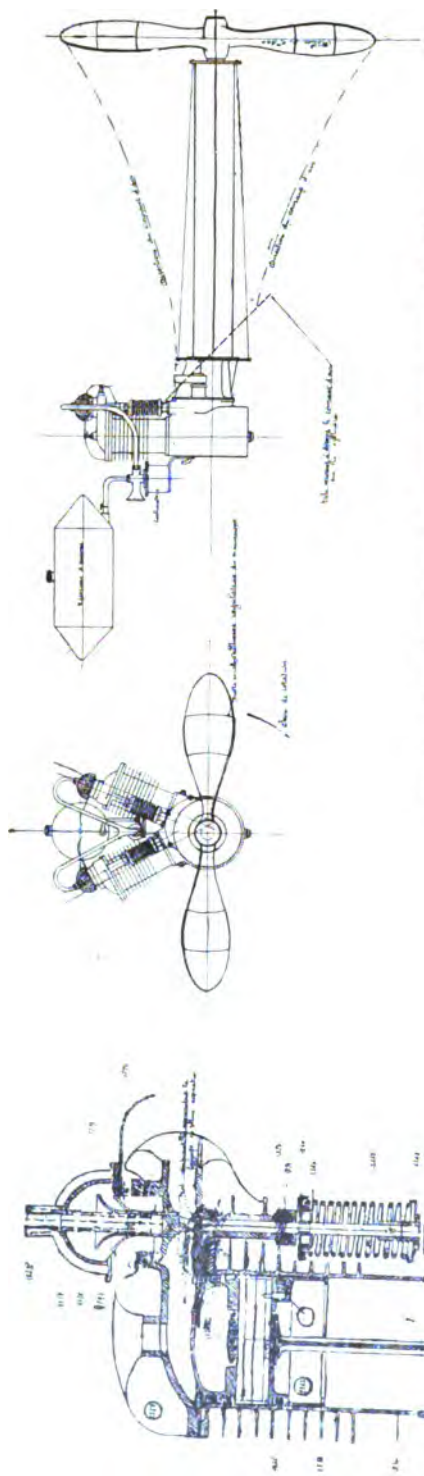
Vue d'ensemble d'un groupe aéromoteur de 12 HP.
